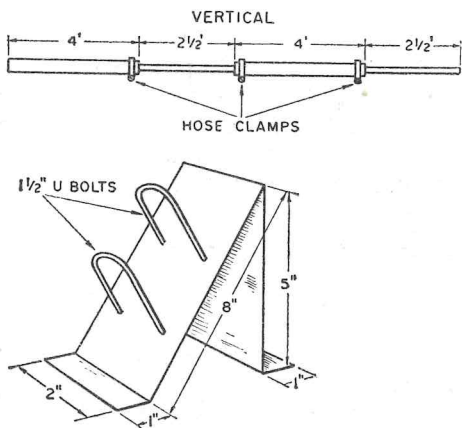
Arriba, elemento radiante vertical; debajo, detalles para la construcción del elemento radiante vertical.
